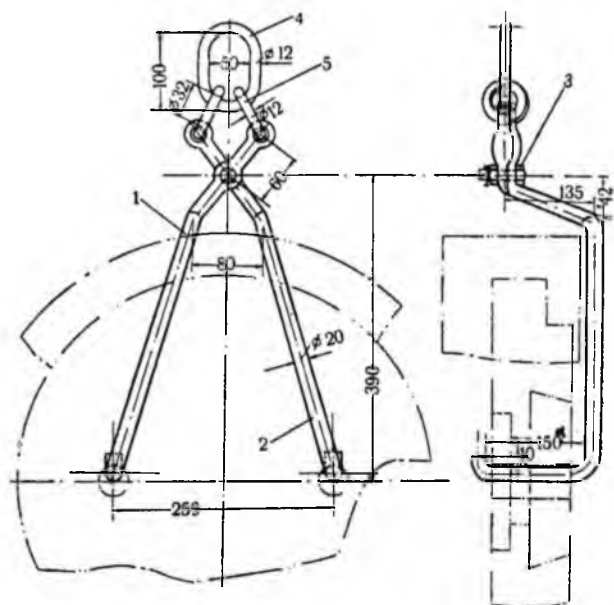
Схватка для маховика СХТЗ-НАТИ:
